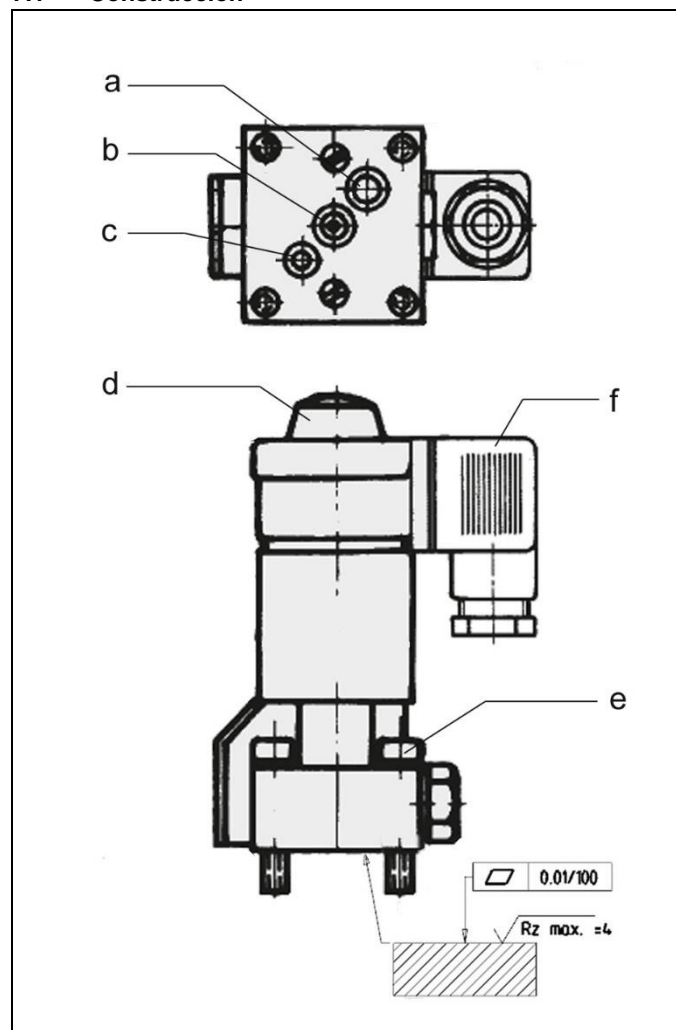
Construcción - válvula distribuidora 2/2 y 3/2
